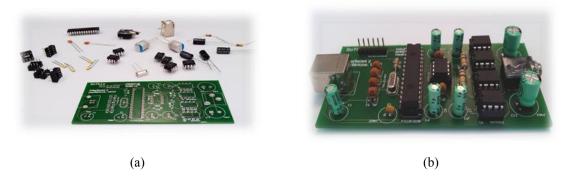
(a) Placa PCB y componentes electrónicos. (b) resultado final.
